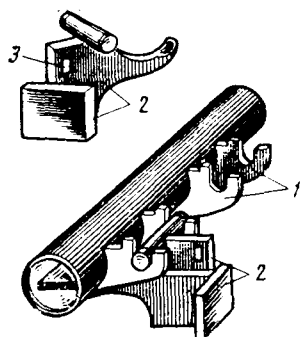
Схема устройства для подвески зубьев на гребке печи ВХЗ:
